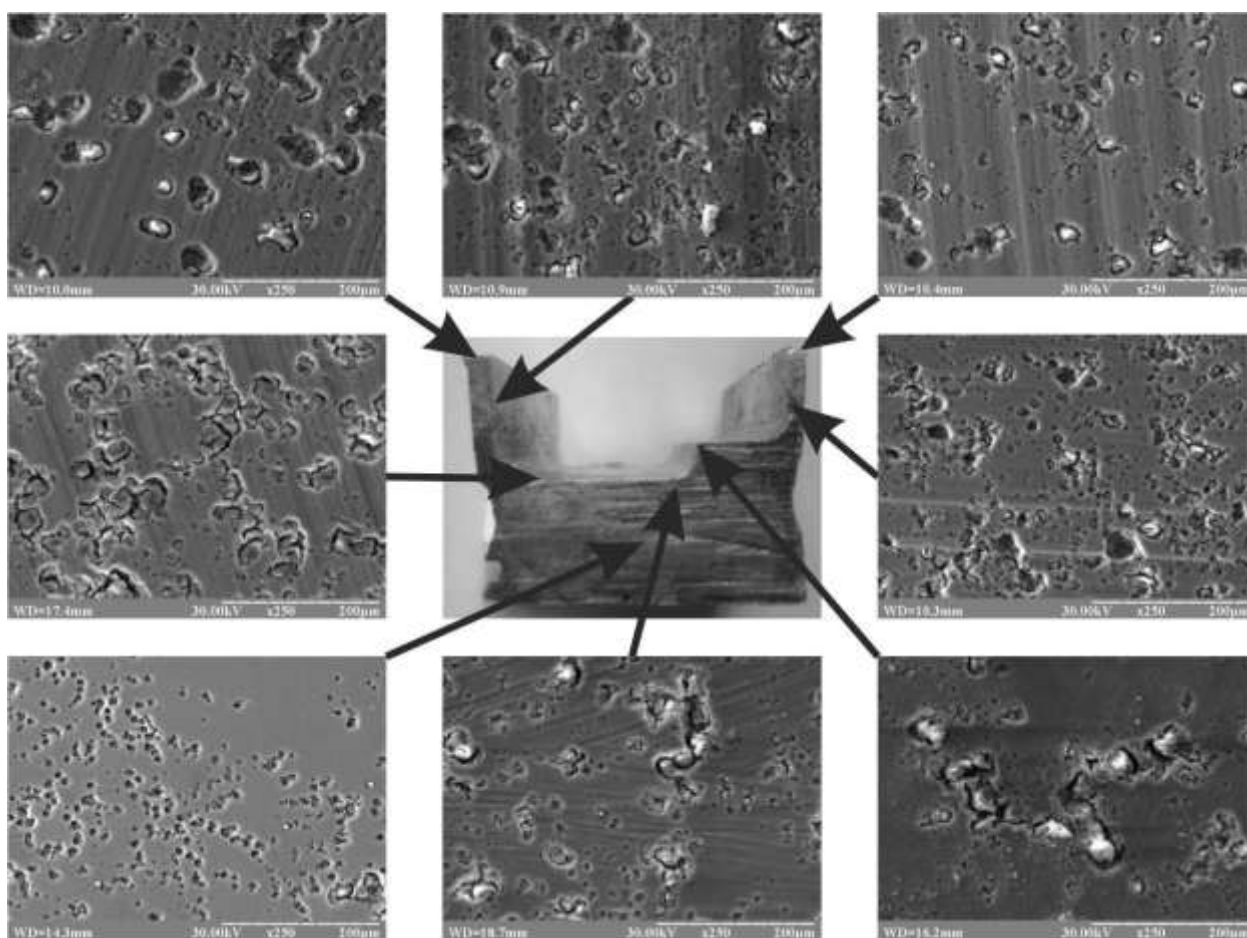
Изображения торца заготовки (в центре) и соответствующих микрошлифов участков заготовки.
